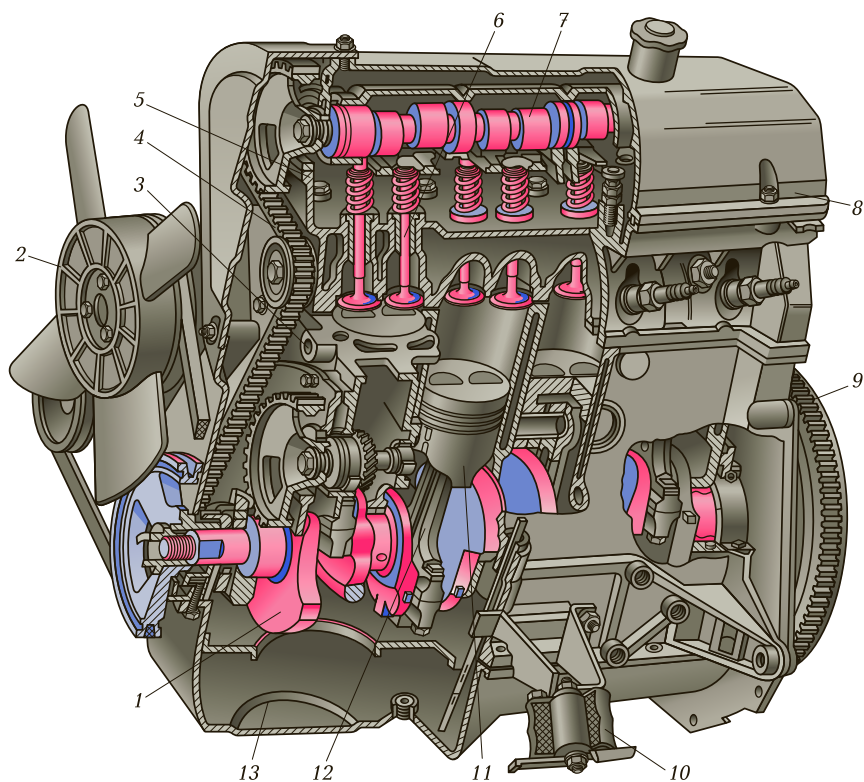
Общий вид двигателя легкового автомобиля:
